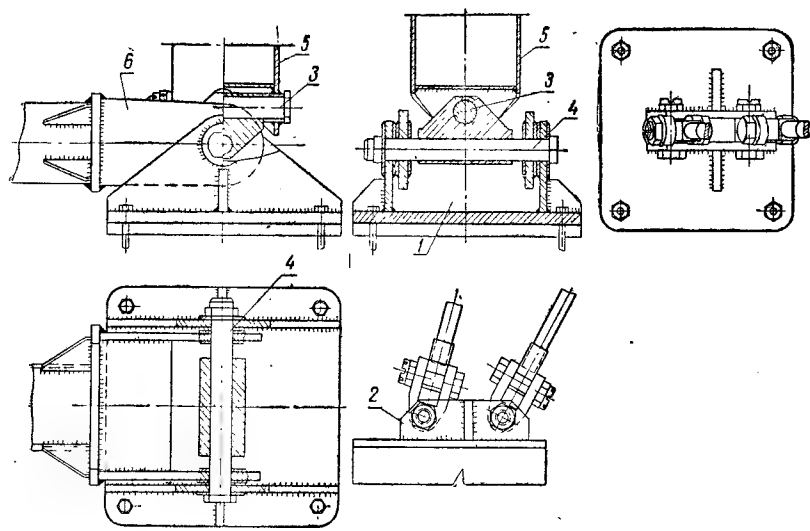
Кронштейны крепления агрегата ВЭС-1-5 на фундаменте:
